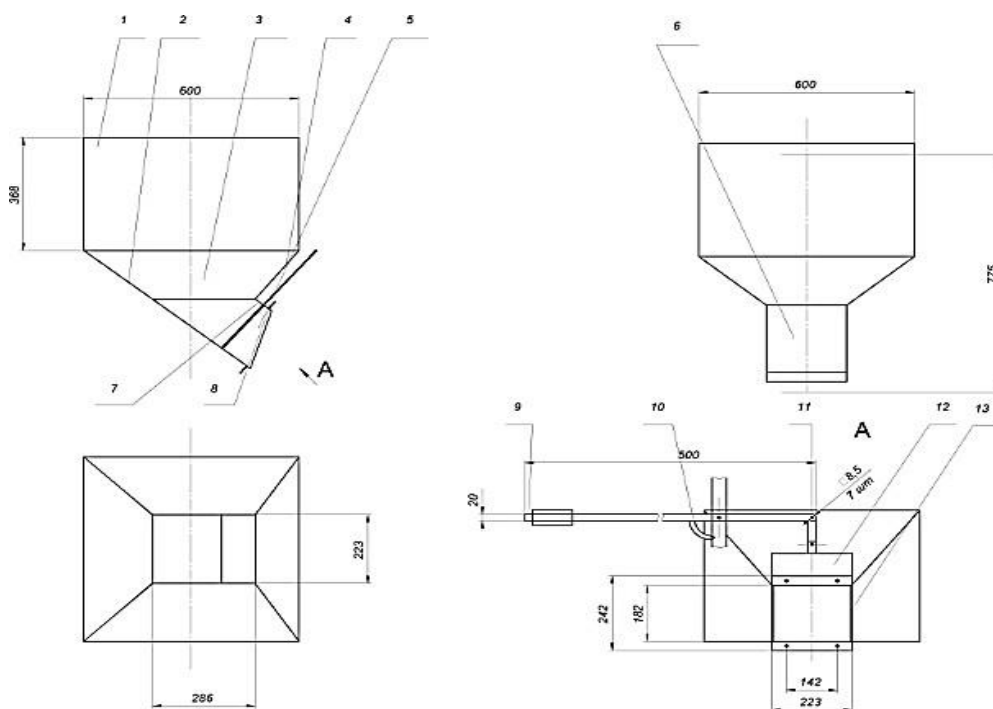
Конструктивна схема загрузочного пристрою машини попереднього очищення зерна
